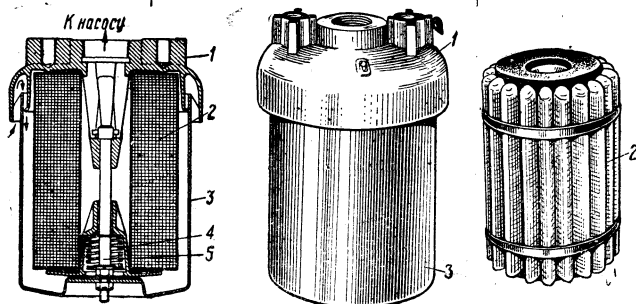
Фильтр всасывающий кросс-компаунд-насоса: 1 — корпус; 2 — фильтровальный патрон; 3 — кожух; 4 — пружина; 5 — стержень
